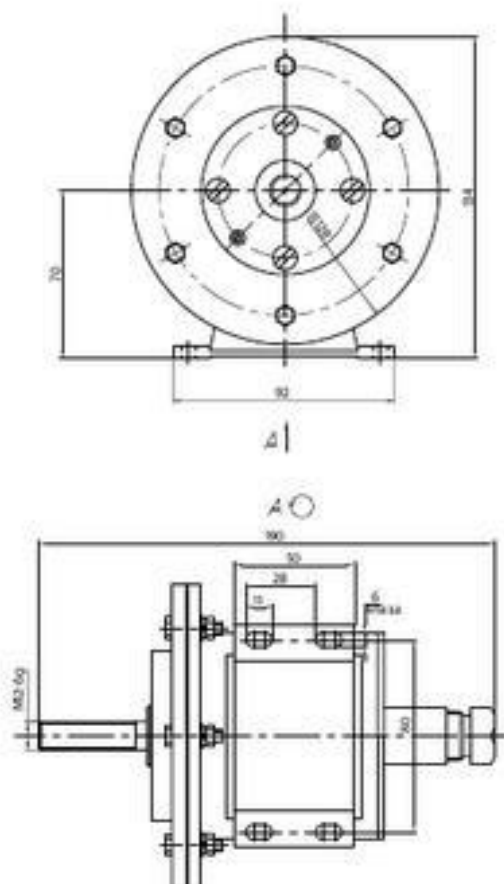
Габаритные и присоединительные размеры III МГДУ УП.
